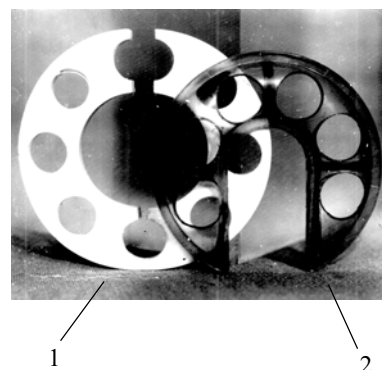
Изолятор: 1 — изготовленный из фторопласта механической обработкой; 2 — изготовленный из темплену литьем под давлением
